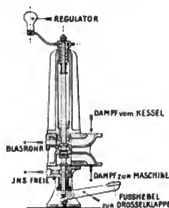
Regulator und Drosselventil des Sentinell-Wagens.
